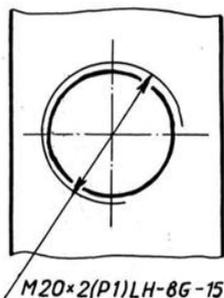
Обозначение двухзаходной внутренней метрической резьбы
